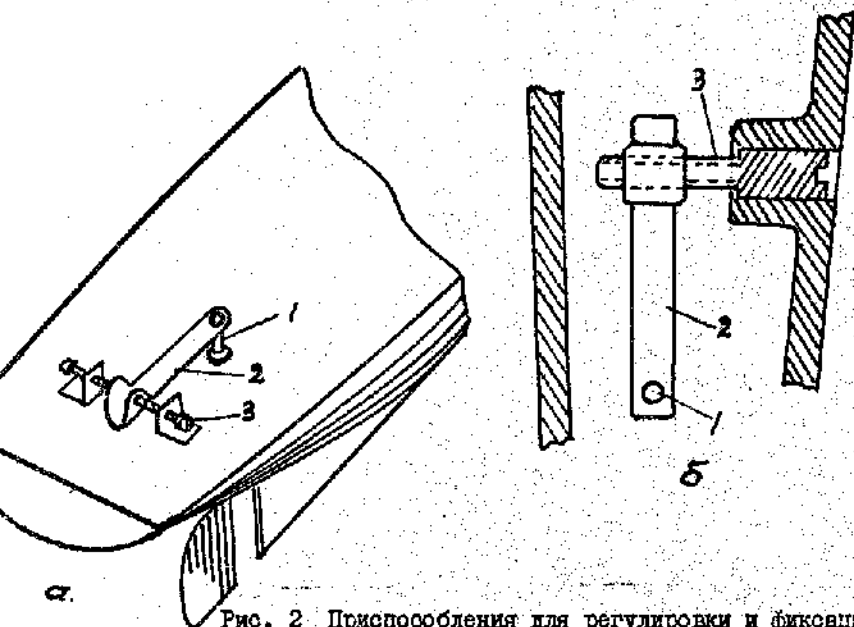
Приспособления для регулировки и фиксации руля: а - на палубе модели; б - в корпусе модели; 1 - баллер; 2 - румпель; 3 - регулировочные винты.
